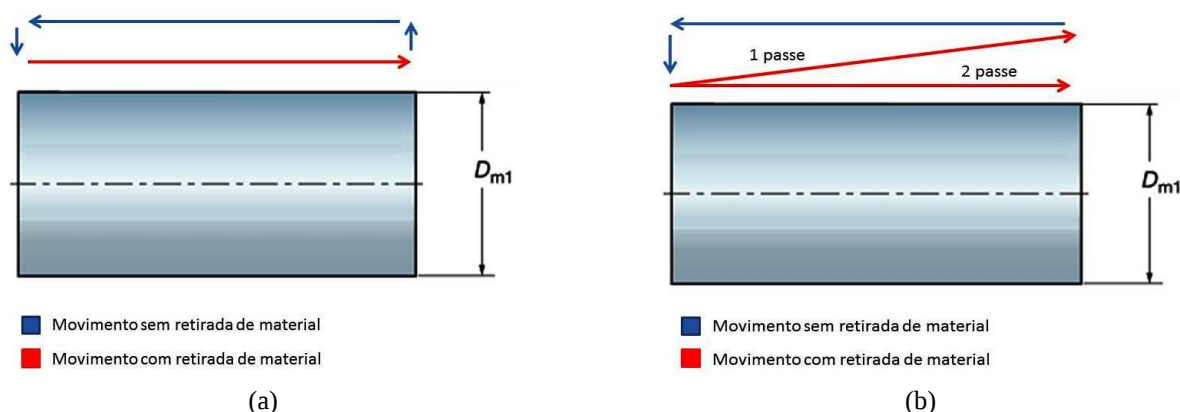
Estratégias de usinagem. (a) Corte longitudinal. (b) Corte cônico ou em rampa.
